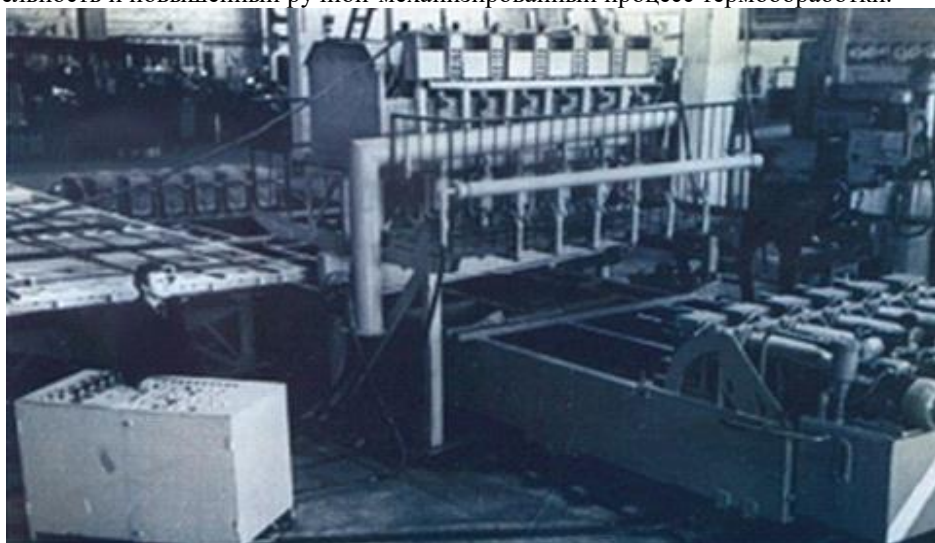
Закалка ручной-механизированной шести ручейной установки готовых насосных штанг
